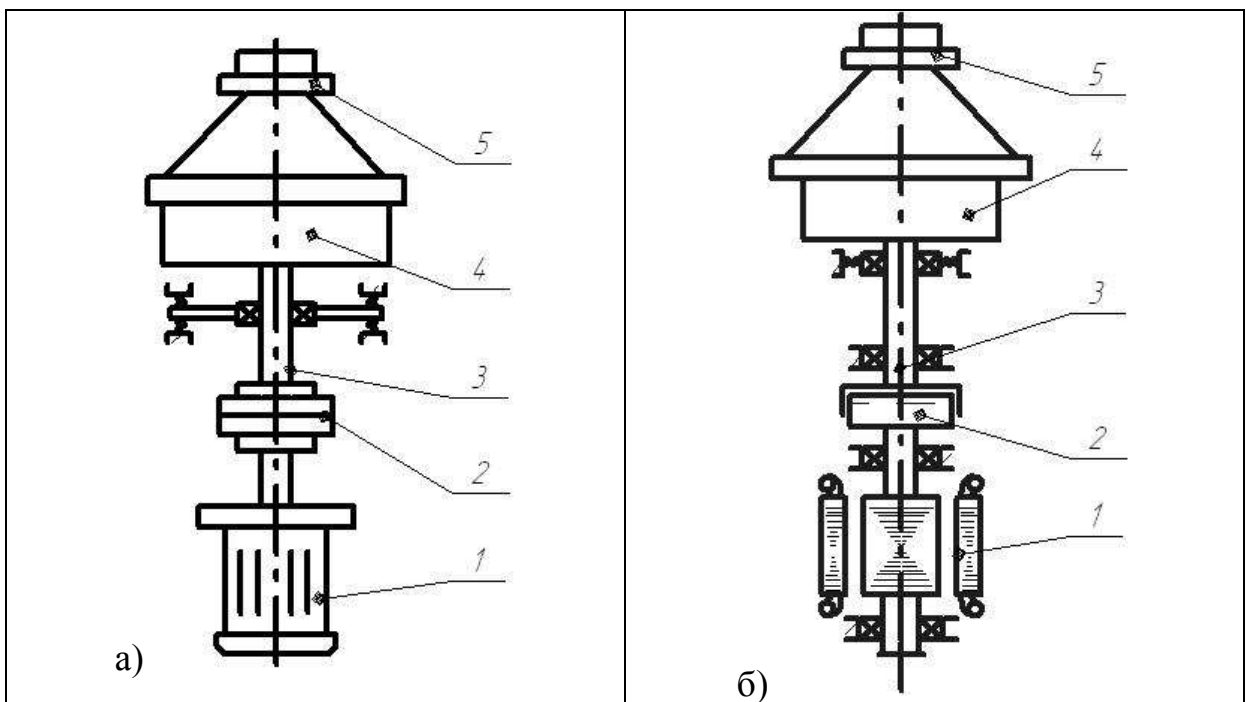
Кинематические схемы безредукторных сепараторов молока:
